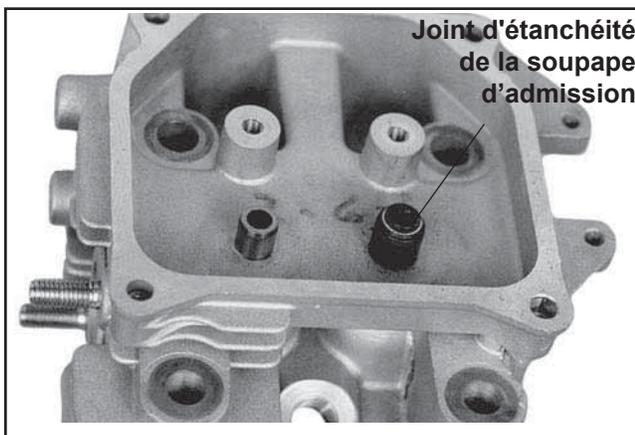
Position du joint d'étanchéité de la soupape d'admission.
